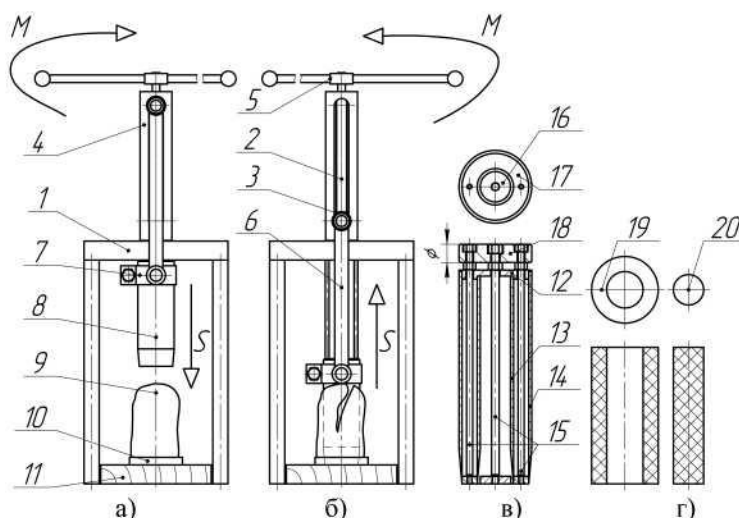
Принципова схема роботи установки (а, б), робочий орган (в) та утворені заготовки (г): 1 - рама; 2 - ходовий гвинт; 3 - гайка; 4 - направляюча; 5 - вороток; 6 - тяги; 7 - зажим; 8 - робочий орган; 9 - продукт; 10 - підставка; 11 - основа; 12 - обойма; 13 - внутрішня висічка; 14 - зовнішня висічка; 15 - шпильки; 16 - виштовхуюча шайба; 17 - виштовхуюче кільце; 18 - поперечина; 19, 20 - трубовидна та циліндрична заготовки.
